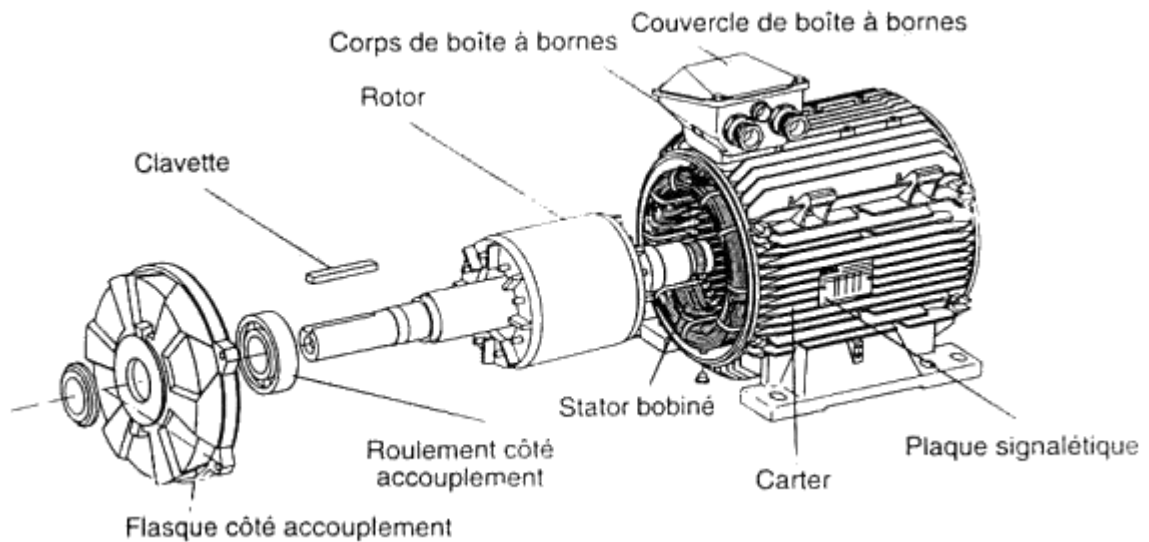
Vue éclatée d'une machine asynchrone double étoile
